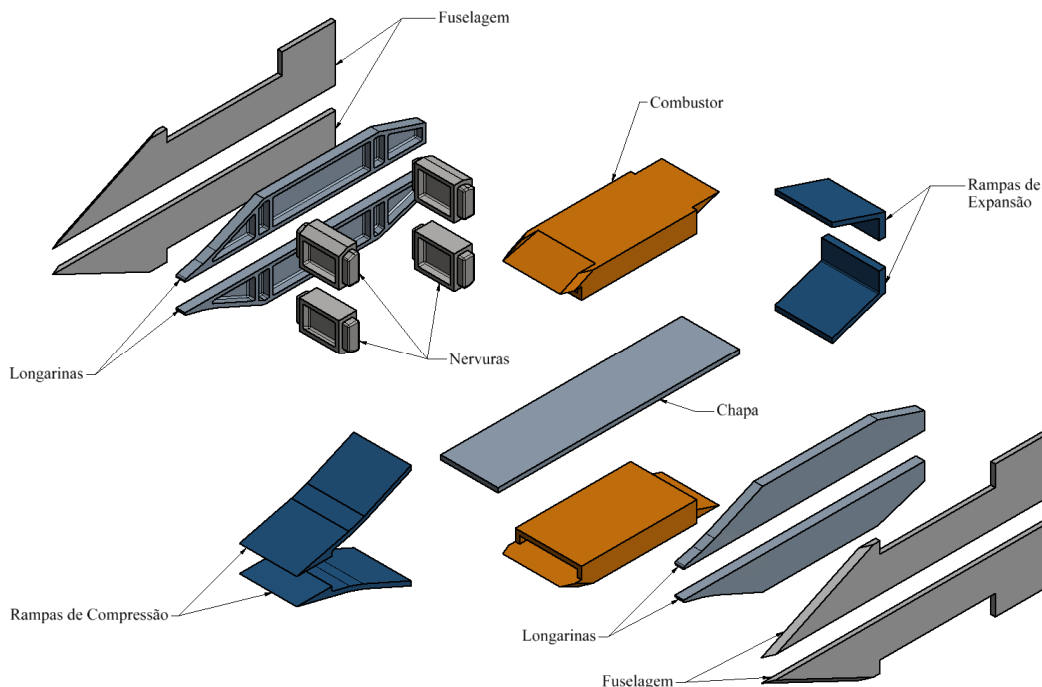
Vista Explodida do Scramjet de Simetria Planar
